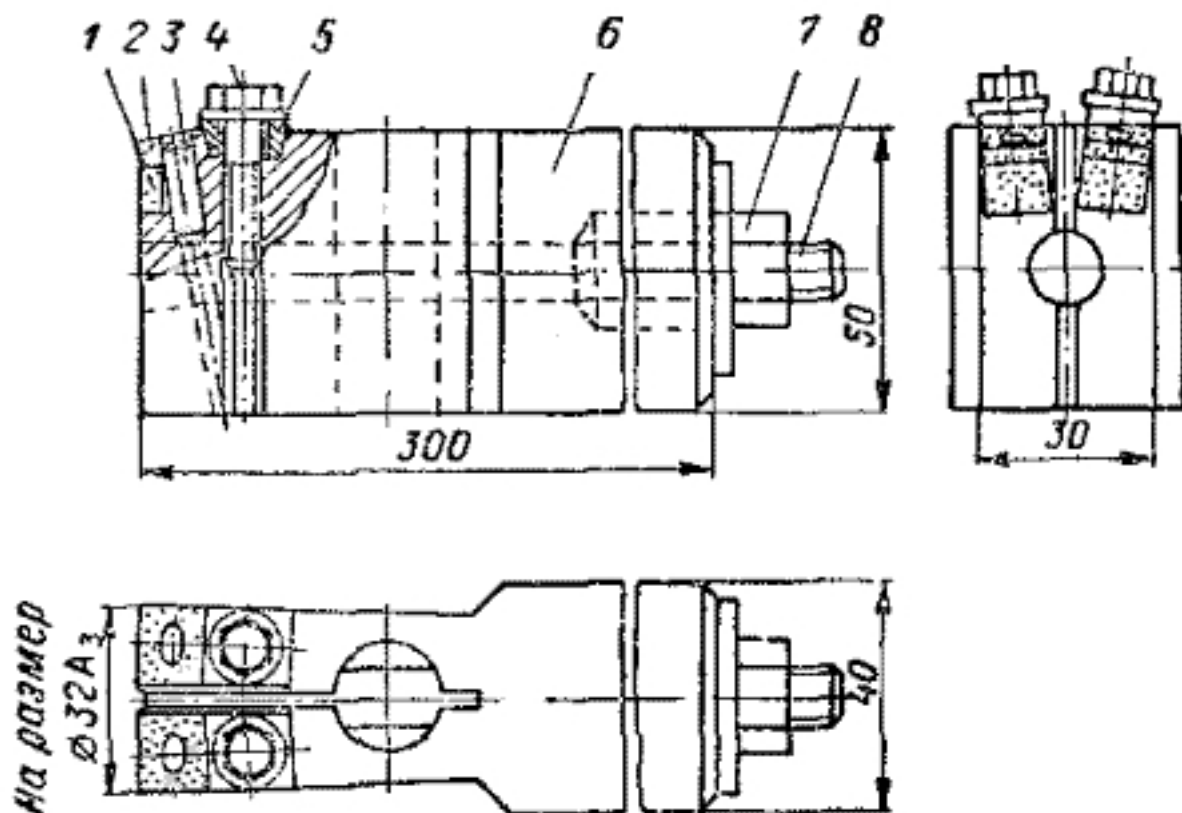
Калибровочный резец с четырехгранными пластинками.
